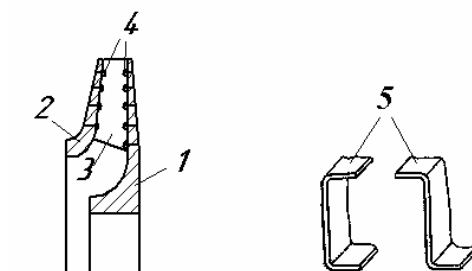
Закрытое РК со штампованными лопатками: 1 — основной диск; 2 — покрывающий диск; 3 — лопатка; 4 — заклепки; 5 — различные формы отбортовок
